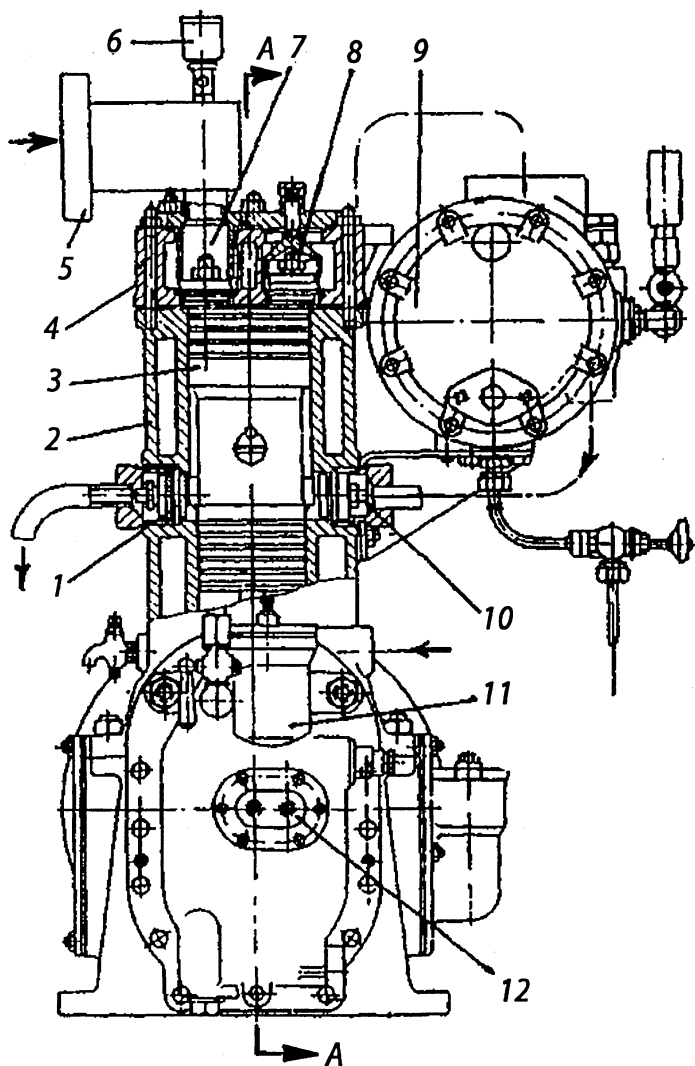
Компрессор фирмы «Бурмейстер и Вайн»: 1 — нагнетательный клапан второй ступени, 2 — блок цилиндра, 3 — поршень, 4 — крышка цилиндра, 5 — входной воздушный фильтр, 6 — капельная масленка для смазки цилиндра первой ступени, 7 — всасывающий клапан первой ступени, 8 — нагнетательный клапан первой ступени, 9 — воздухоохладитель, 10 — всасывающий клапан второй ступени, 11 — масляный фильтр, 12 — масляный насос
